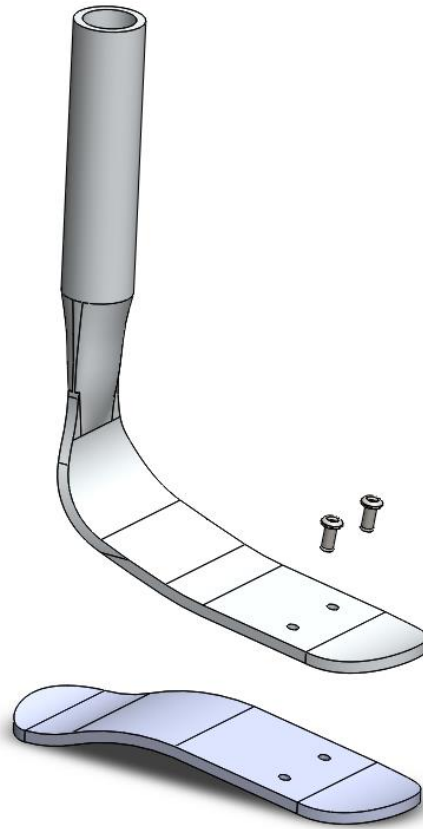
Ensamble prótesis transtibial (vista explotada)
